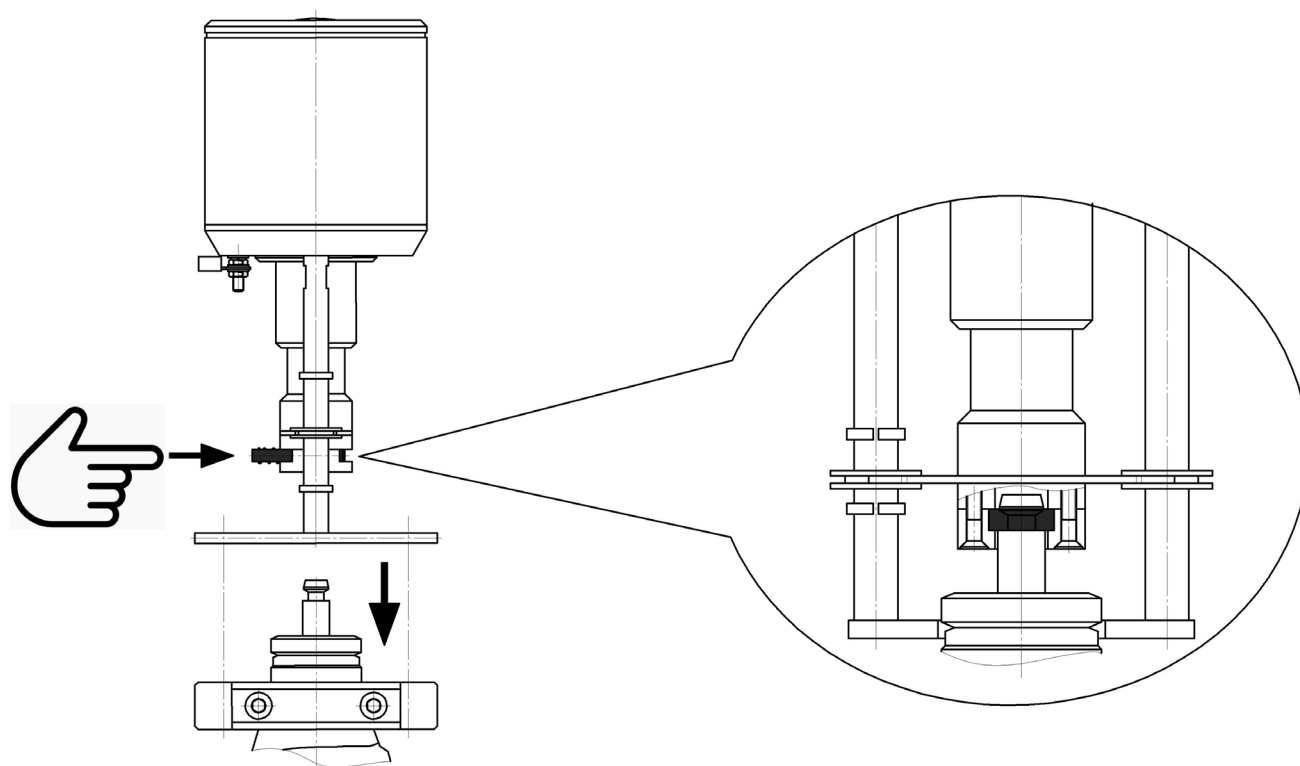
Соединение штока клапана с механизмом захвата привода ЭП-180К при установке
